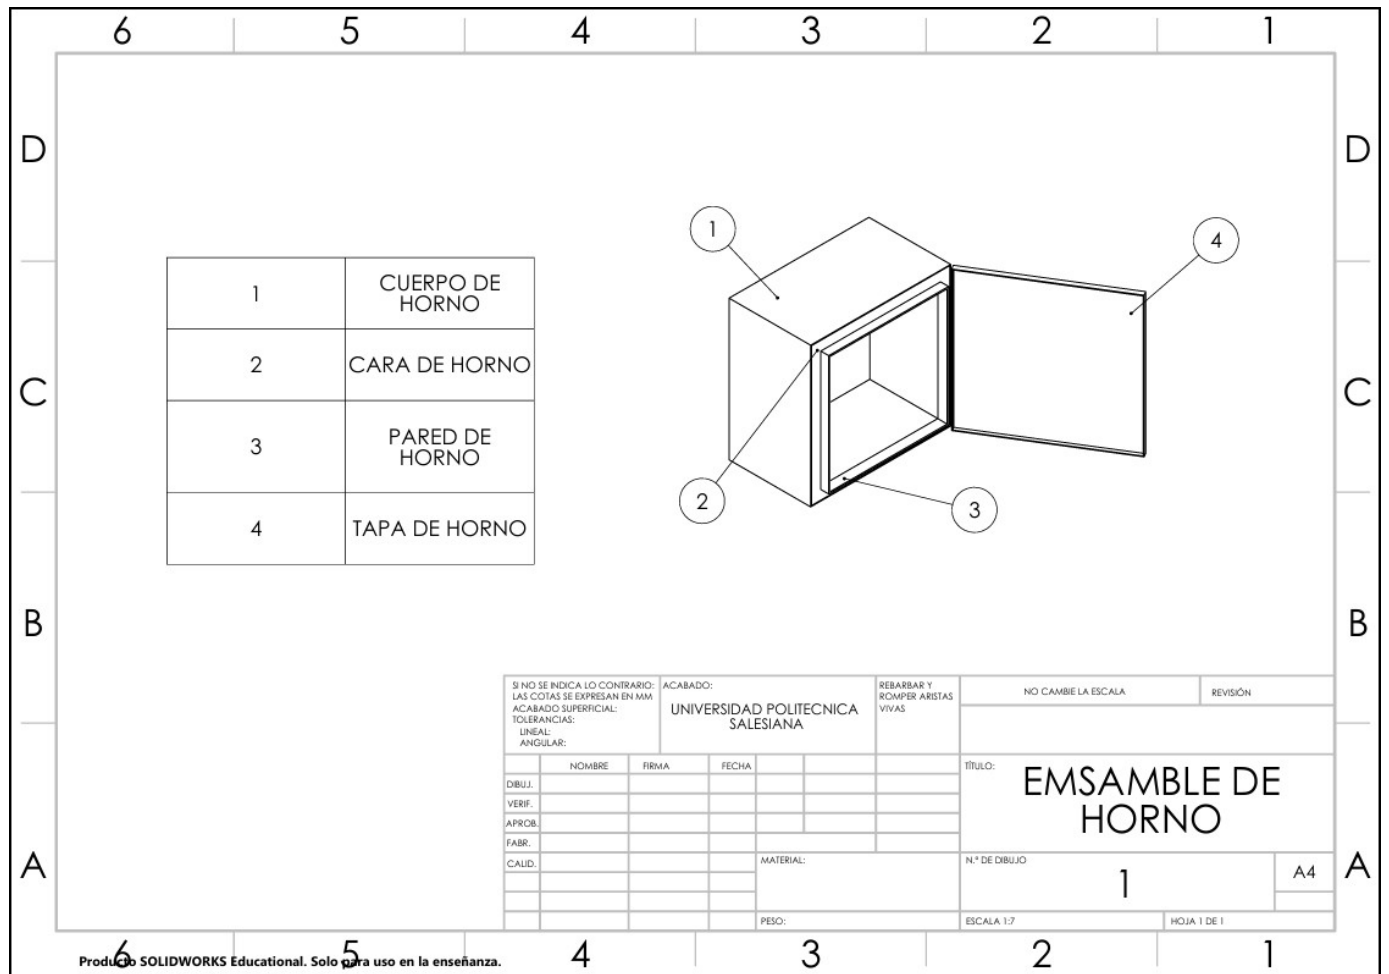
Plano de ensamble general isométrico del horno, diseñado en SolidWorks. Por Autores
